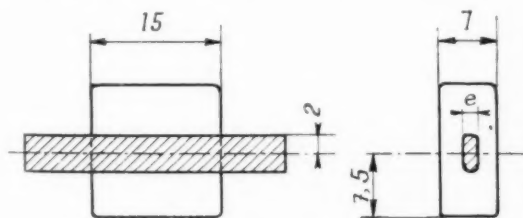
Éprouvettes type C $e = 1; 1,5$.
